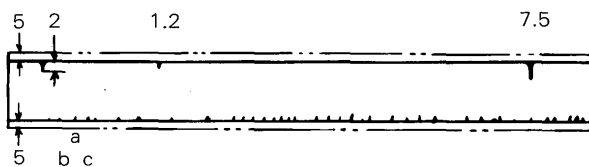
Schweißfläche: Eingußseite (a)
